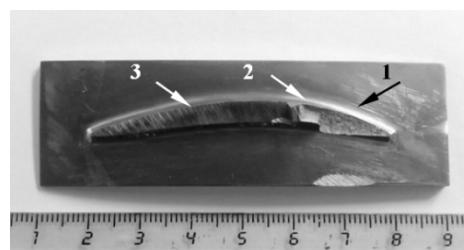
Общий вид сегментов блиска. Место сварного соединения показано стрелкой:
